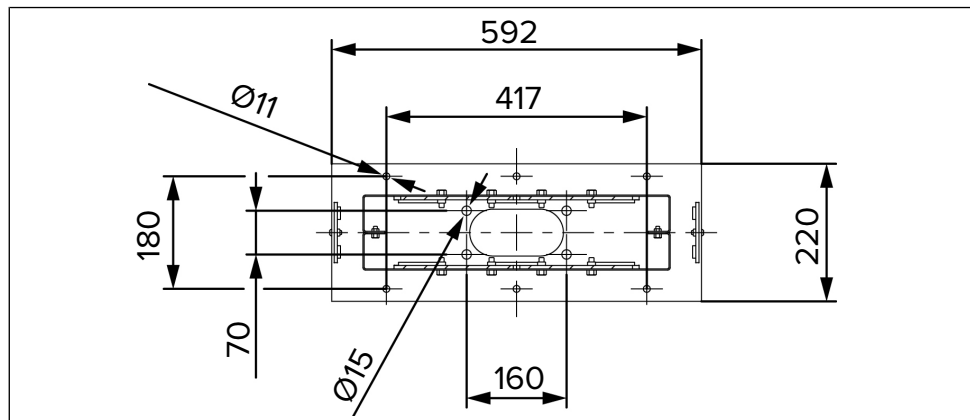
Dimensions de la plaque adaptatrice 18591
